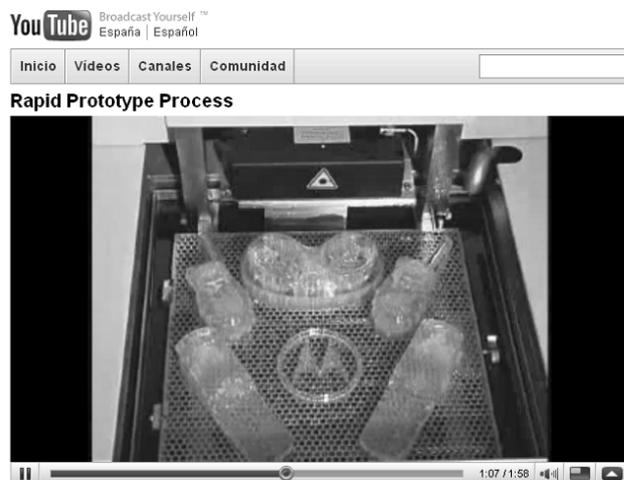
Instantánea del vídeo “Rapid Prototype Process” que muestra la técnica de prototipado de Motorola [9].
